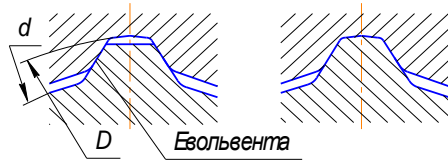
Шліцеве з'єднання з евольвентними зубами: а - центрування по бокових гранях b ; б - центрування по зовнішньому діаметру D
